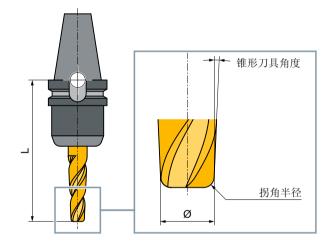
3D 刀具,例如:带倒圆的截锥铣刀(156型)
